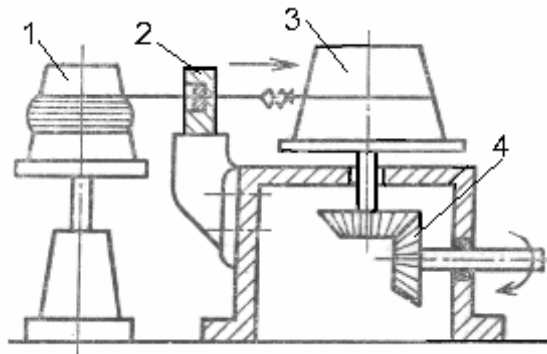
Барабанный волочильный стан: 1 – вертушка с бунтом проволоки; 2 – волока; 3 – барабан; 4 – зубчатая передача
